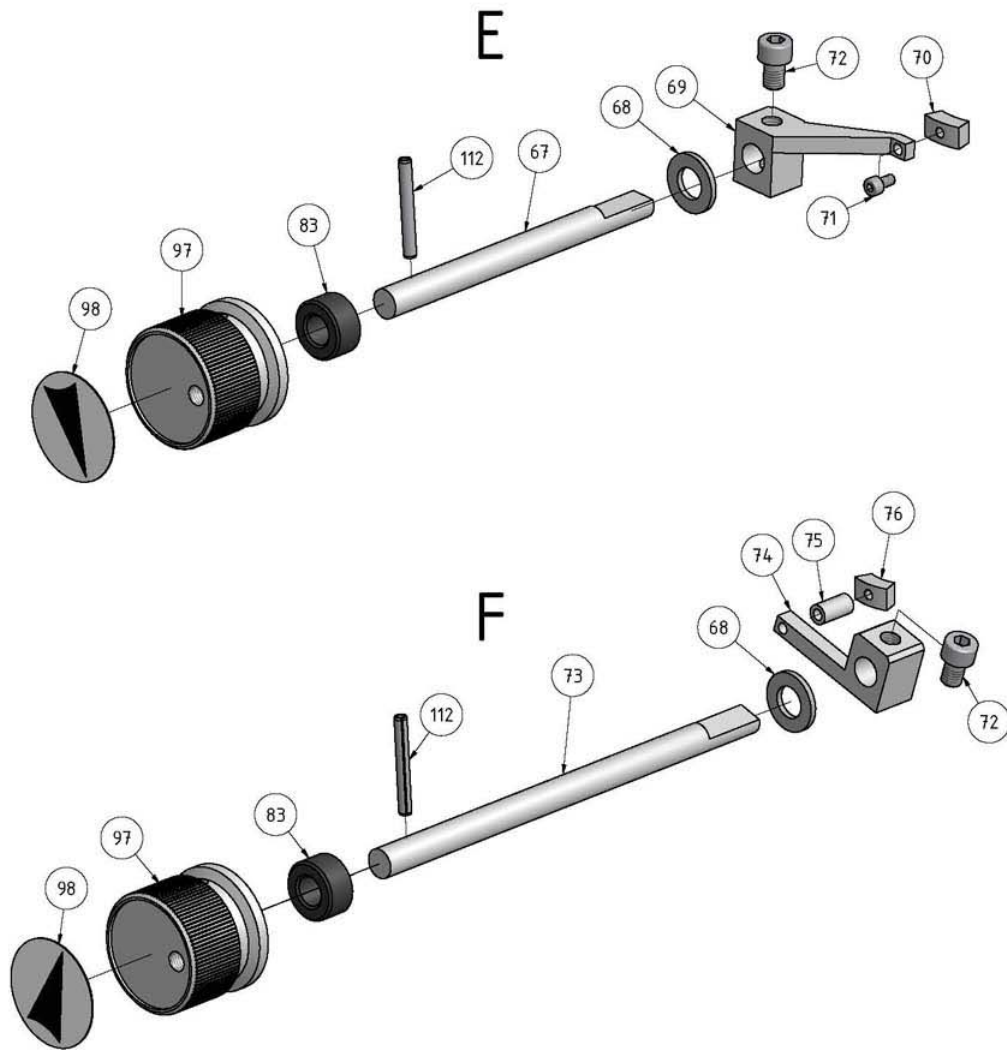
Fräskopf 4 von 6 - Milling head 4 von 6
